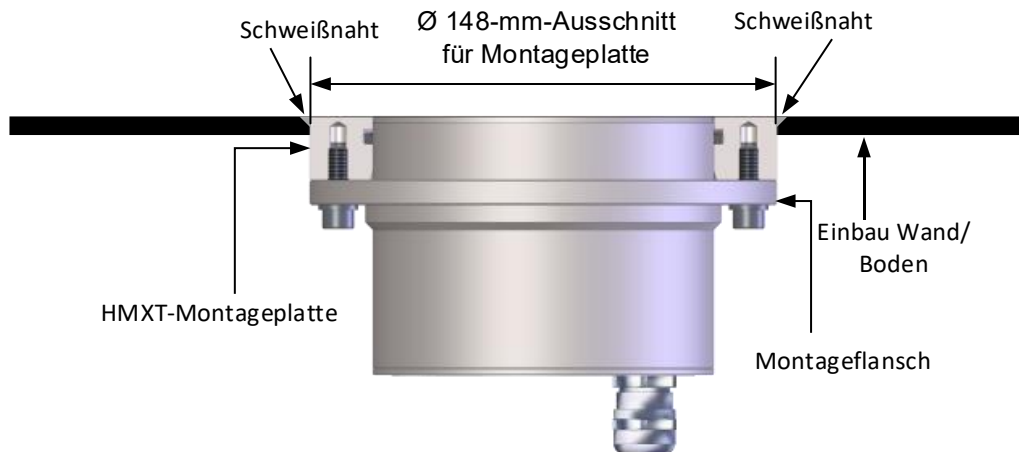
Einbau des Sensors (Bündig montierte Montageplatte)
